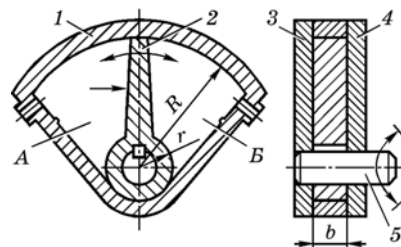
Схема однопластинчастого поворотного гідродвигуна:
